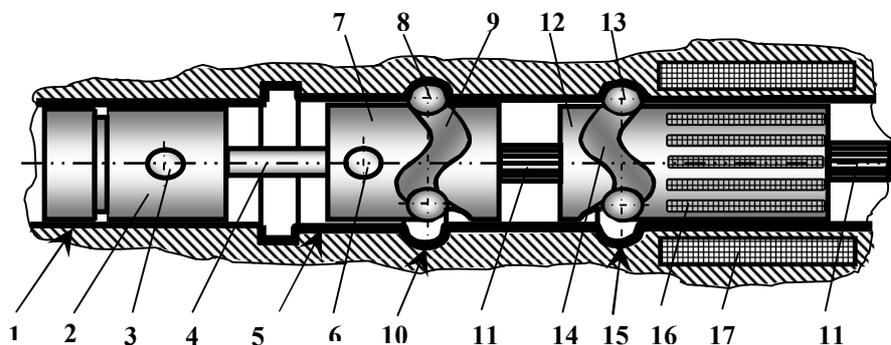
Конструктивная схема компрессора с кулачковым приводом, выполненным в виде кулачка с синусоидальной канавкой: 1. Цилиндр. 2. Поршень с газовым подвесом. 3. Верхний шарнир крепления поршня. 4. Шток. 5. Корпус направляющей. 6. Нижний шарнир крепления поршня. 7. Верхний кулачок. 8, 13. Комплект шариков (сепараторы условно не показаны). 9 «Прямая» синусоидальная канавка. 10. Круговая канавка. 11. Шлицевой вал. 12. Нижний кулачок со шлицевым отверстием. 14. «Ответная» синусоидальная канавка. 15. Круговая канавка. 16. Короткозамкнутые обмотки ротора асинхронного двигателя. 17. Обмотки статора асинхронного двигателя
